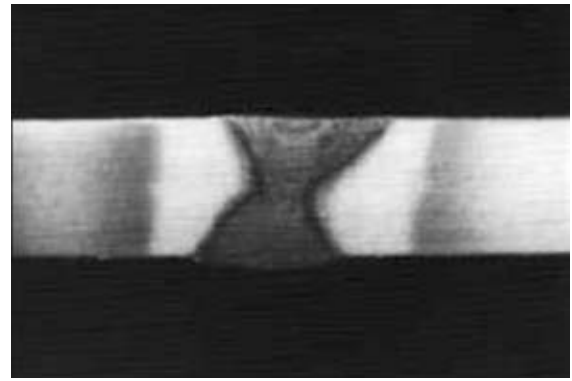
Макрошлиф поперечного сечения шва, выполненного сваркой ТИГ на токе 120 А
